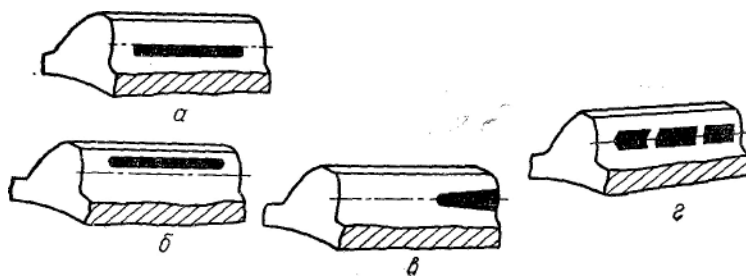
Похибки збірки циліндричної зубчатої передачі.
